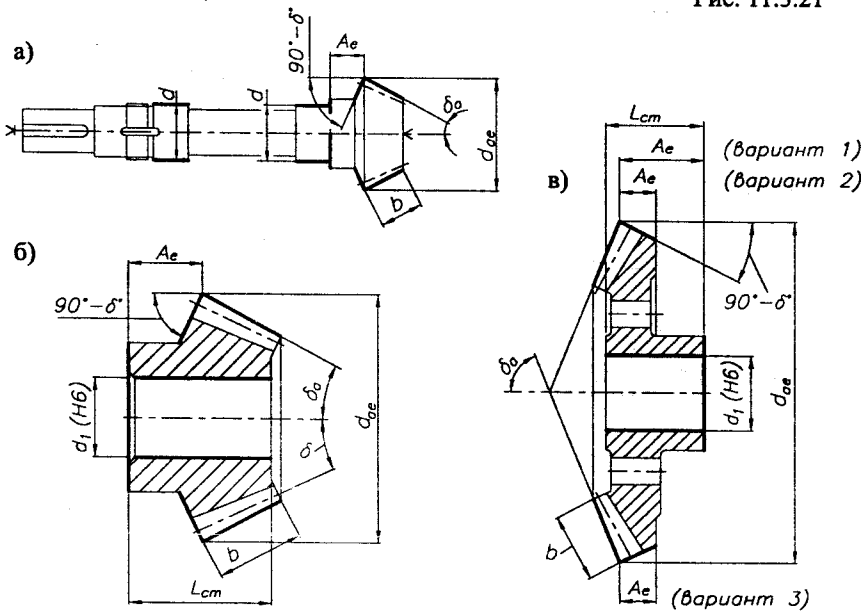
Размеры, требующие указания точности, для заготовок: а) вал-шестерни; б) шестерни; в) колеса
